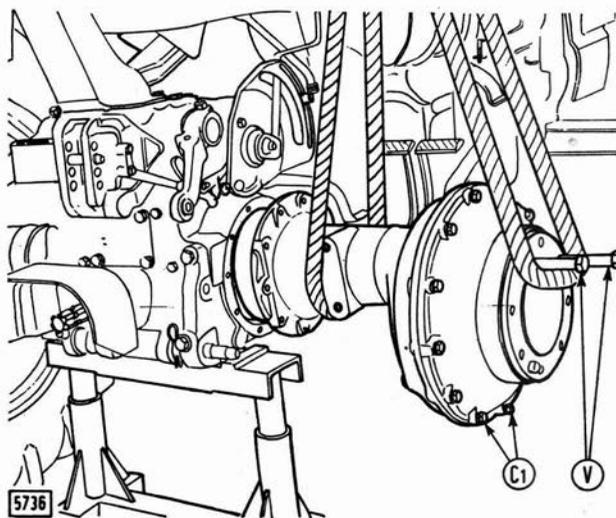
Dépose (remontage) du groupe réducteur latéral droit complet.
